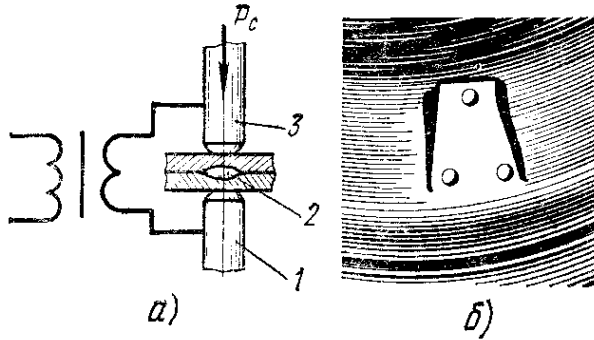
Схема точечной сварки (а) и сварные точки (б)
